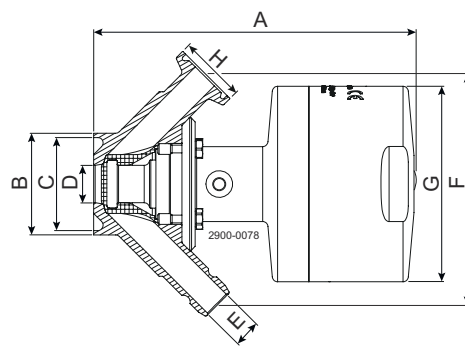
Pneumatisch mit Ventilgehäuse: Rohr mit Kragen Schweißen
